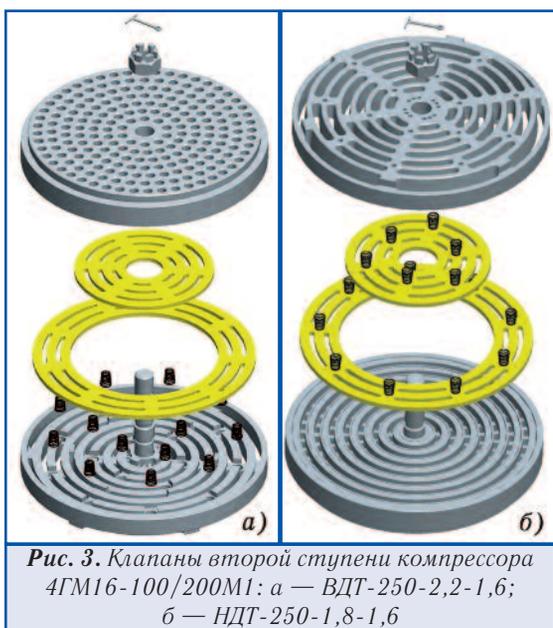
Клапаны второй ступени компрессора 4GM16-100/200M1: а — ВДТ-250-2,2-1,6; б — НДТ-250-1,8-1,6
